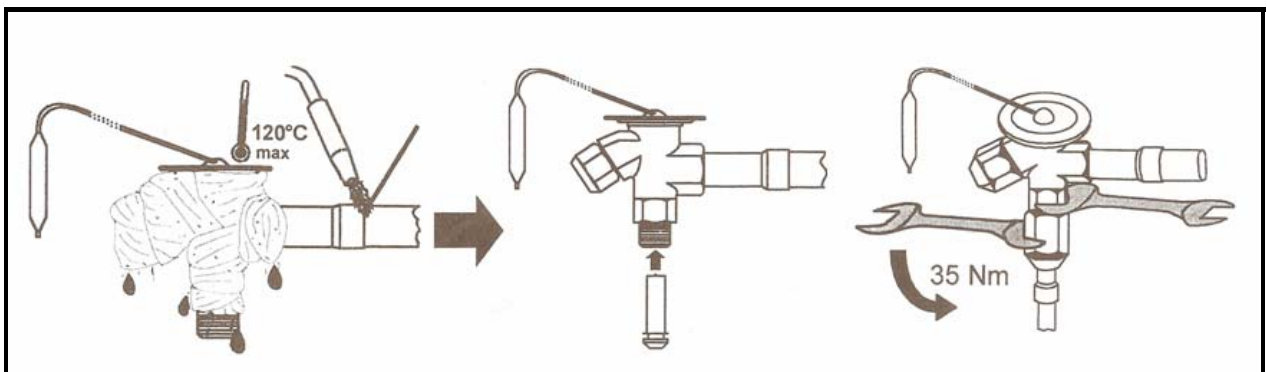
Soldadura y conexión válvula termostática
